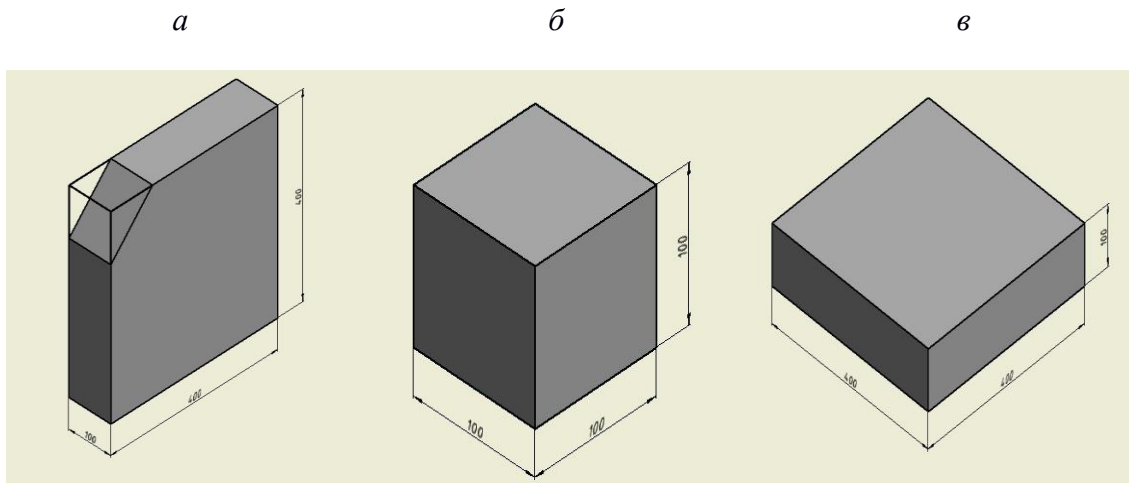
Блоки КА с различными значениями фактора формы:
